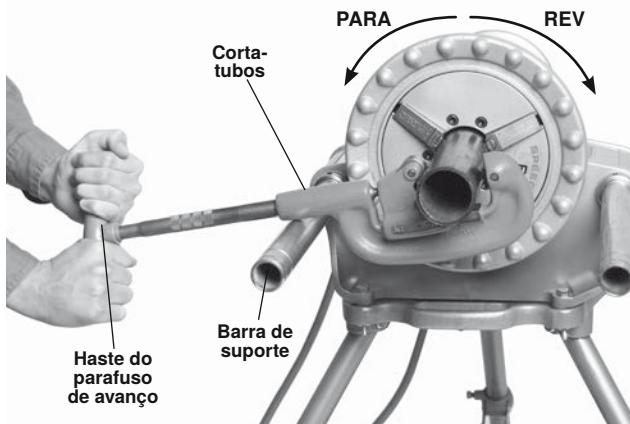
Cortadora de tubos com rotação do cortadora manual/máquina (manter o cortadora em contacto com a barra de suporte).
